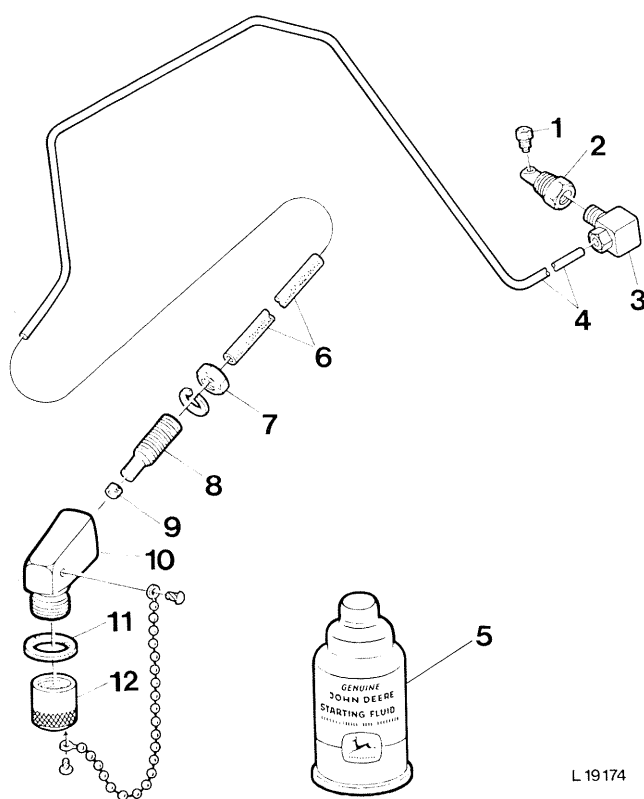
Vue éclatée du dispositif d'aide au démarrage par injection d'éther
